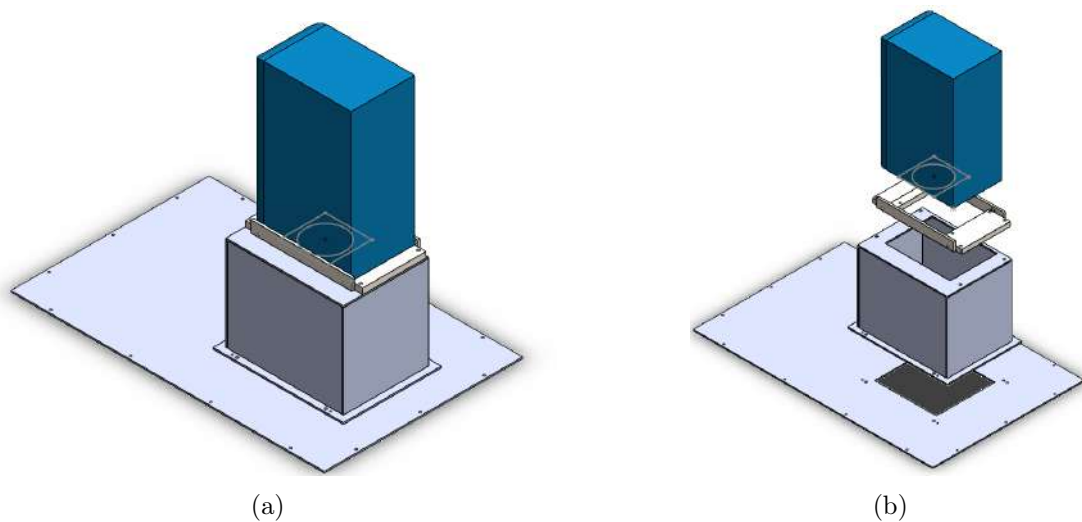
Modelação 3D: (a) Vista isométrica do espaçador do laser com os seus componentes relevantes, (b) Vista explodida parcial do conjunto
